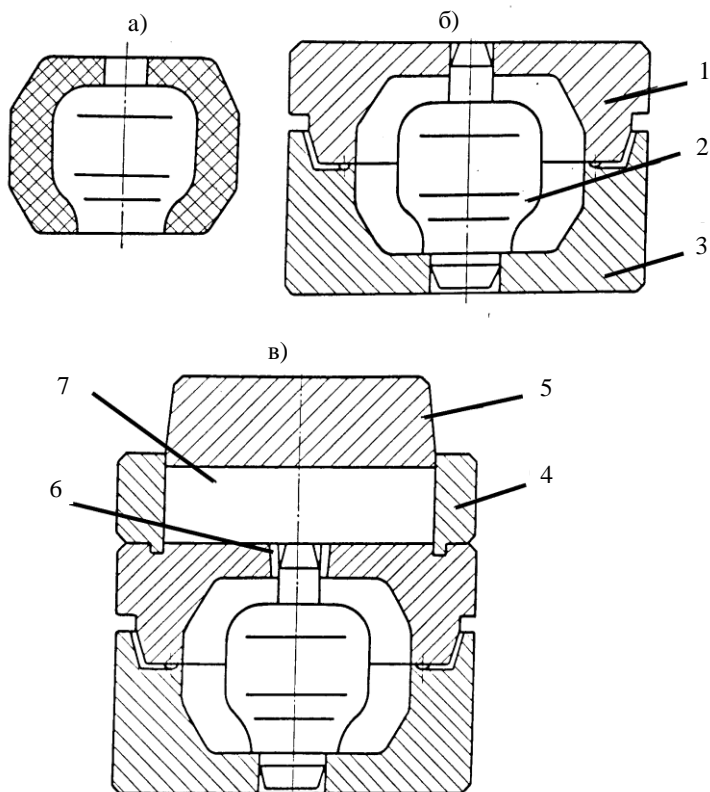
Распространенные типы прессформ (а – резиновое изделие; б – прессформа для плунжерного прессования; в – прессформа для плунжерно-литьевого прессования):
